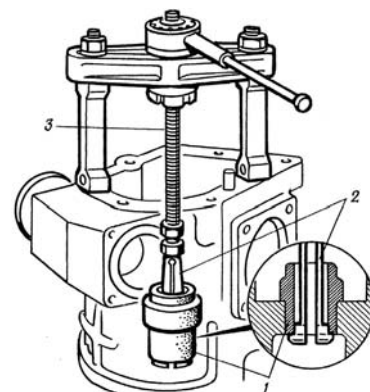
Выпрессовка втулки поворотного вала: 1 — втулка; 2 — цапфа; 3 — винт съемника.
